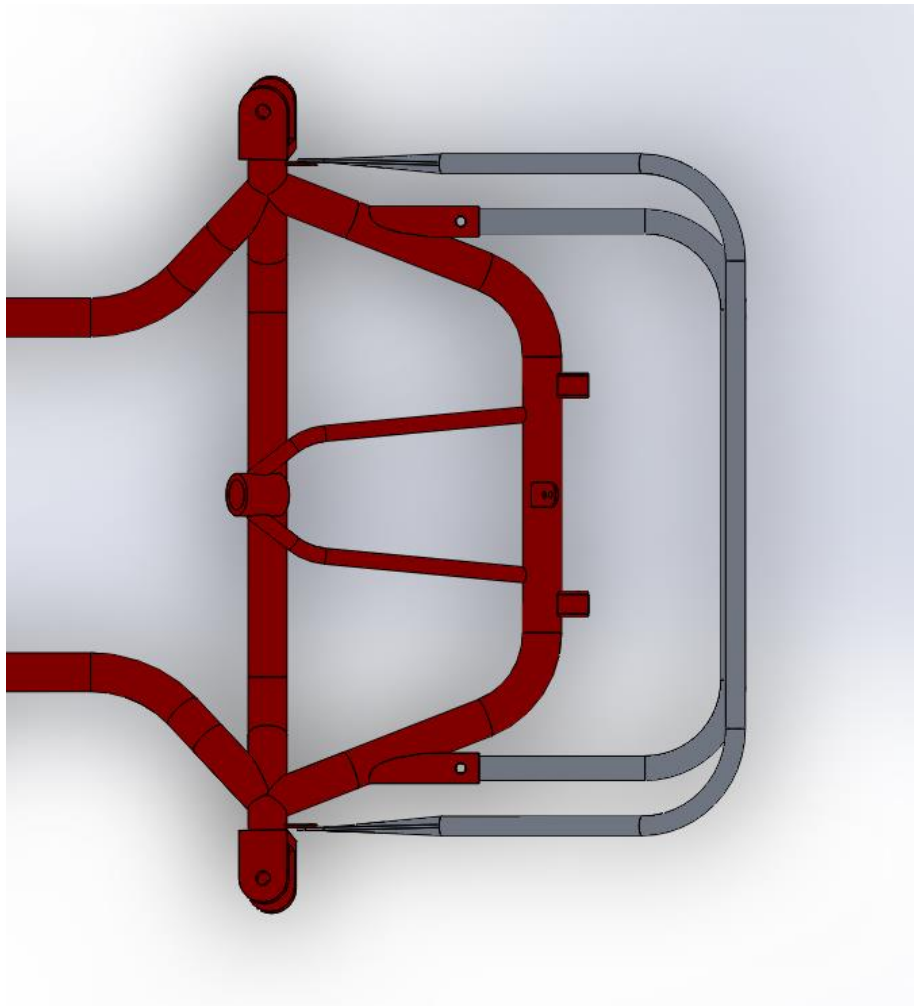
vista superior del conjunto de paragolpes frontal. Fuente: propia.
